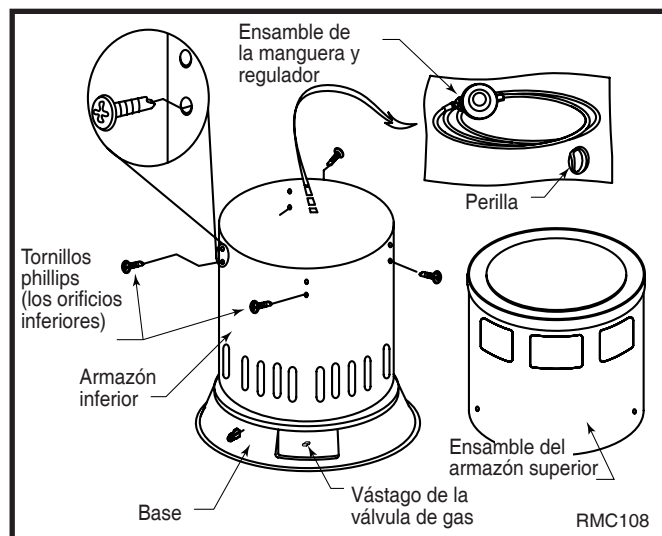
Saque el conjunto de la manguera con regulador, coloque cuatro tornillos en los agujeros de la parte superior de la sección inferior de la carcasa.
